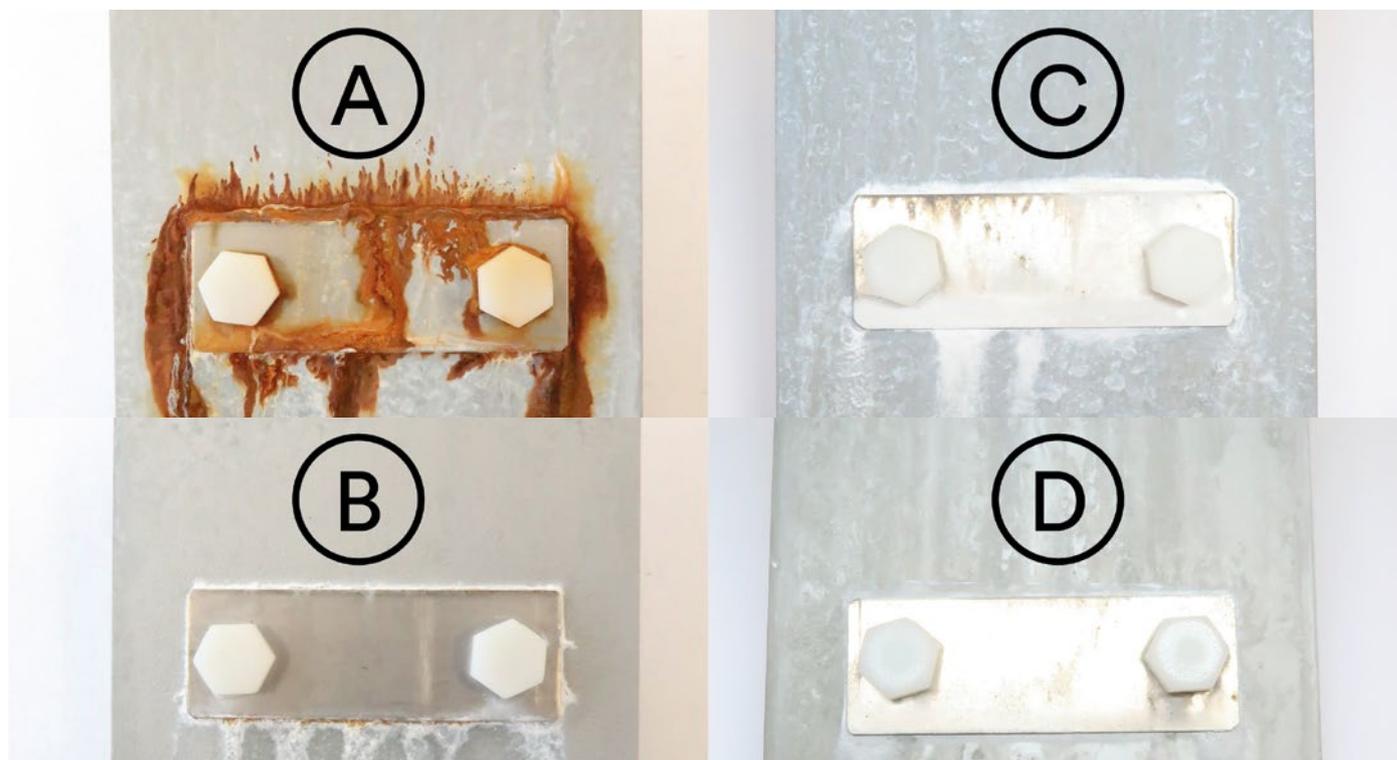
Ergebnisse nach 1.200 Stunden im Salzprühtest. Das große Blech ist mit der Zinklamelle beschichtet, das kleine Blech ist der Kontaktpartner. Zinklamelle mit Basecoat + Edelstahl (A), Zinklamelle mit Basecoat und Topcoat + Edelstahl (B), Zinklamelle mit Basecoat + Aluminium (C), Zinklamelle mit Basecoat und Topcoat + Aluminium (D)
